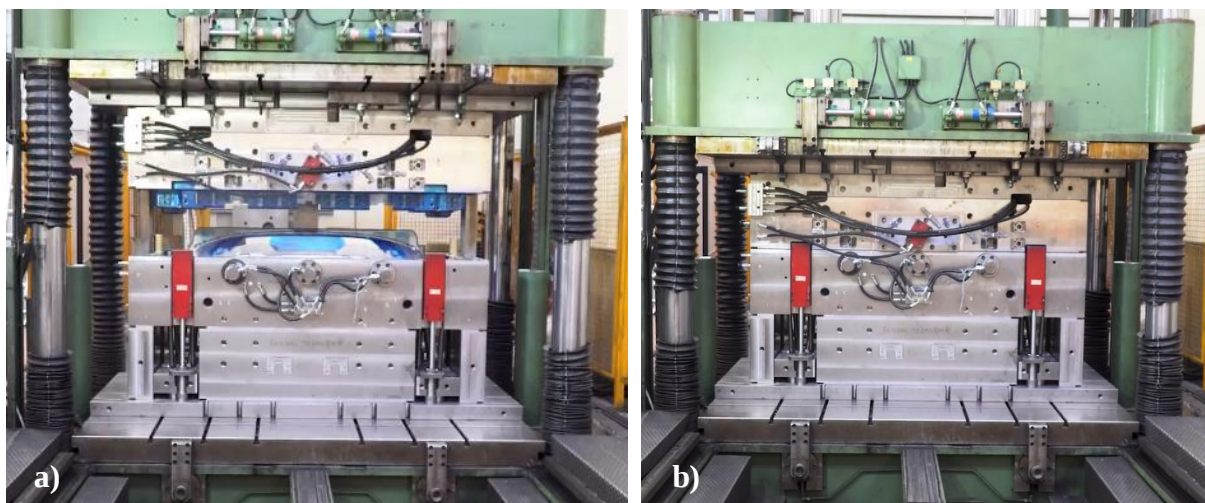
Molde a ser testado na prensa: a) Molde aberto; b) Molde fechado [Adaptado de (Moldit)].
